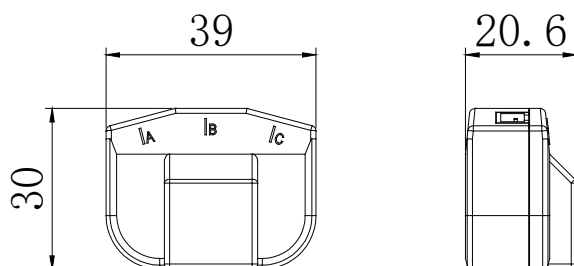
Внешний вид и габаритные размеры модуля коммутации Z1
